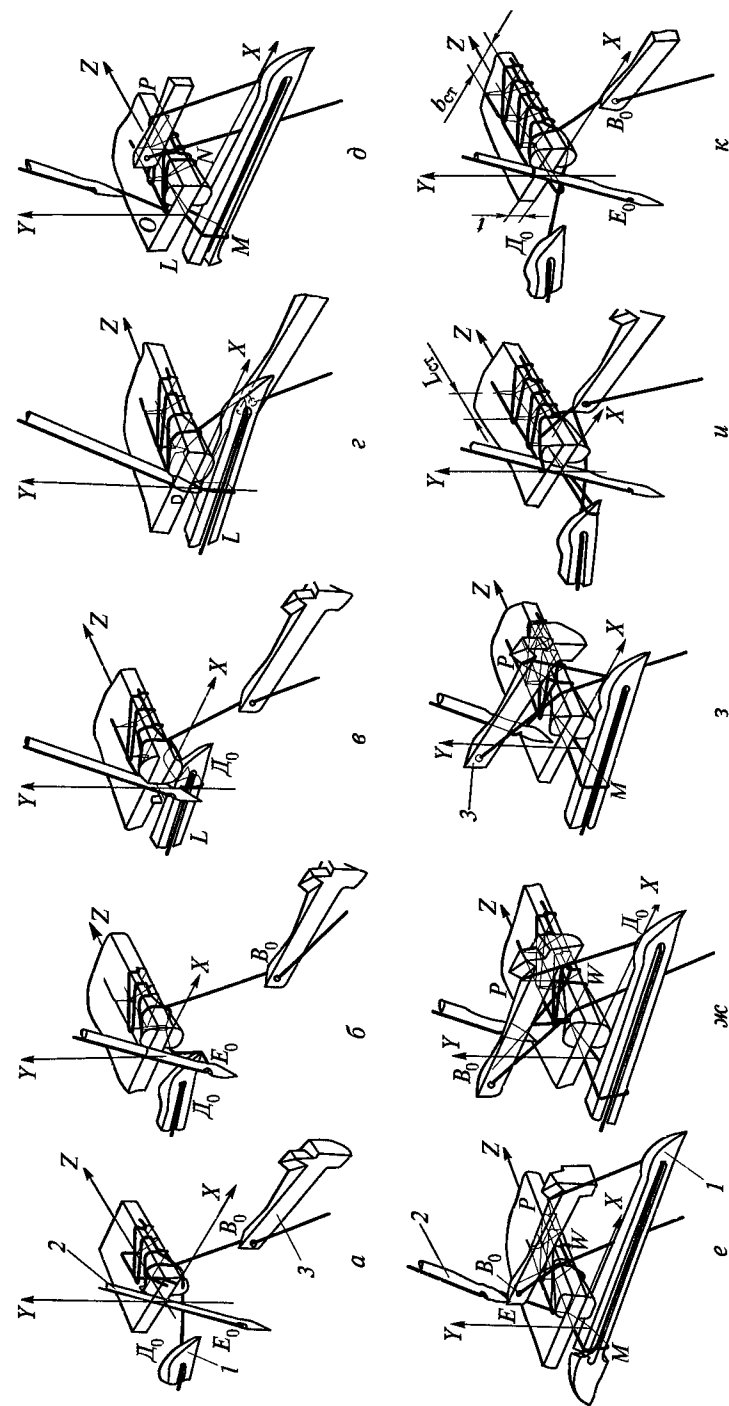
Схемы образования трехниточного краеобметочного стежка типа 504:
